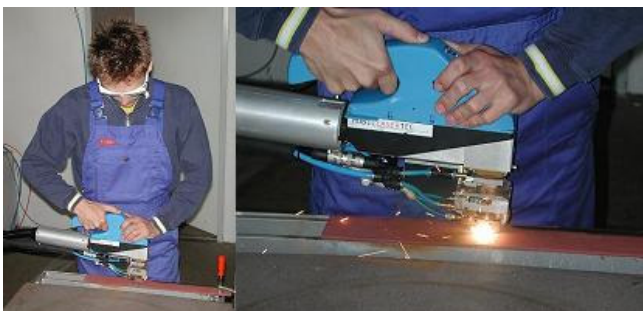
Manuell geführter Laserhandschweißkopf
